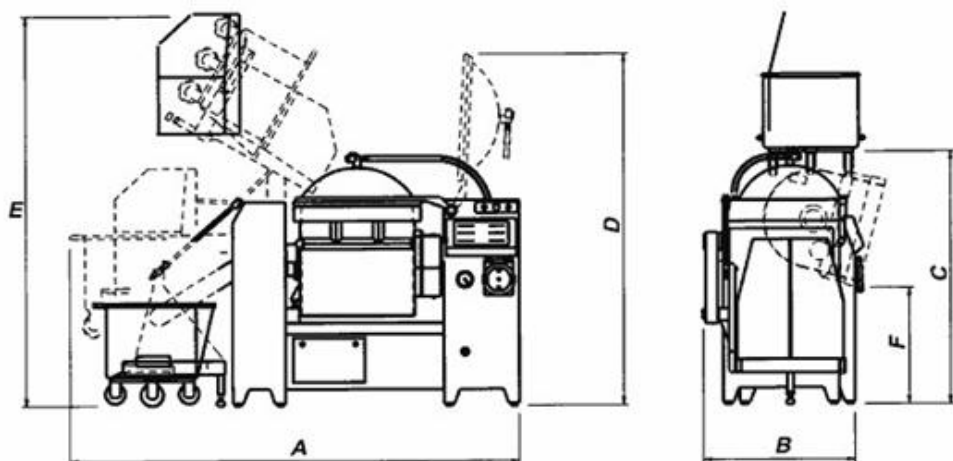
Detall constructiu d'un elevador de columna amb carro de 200 L en una mescladora (CastellVall, 2011)
